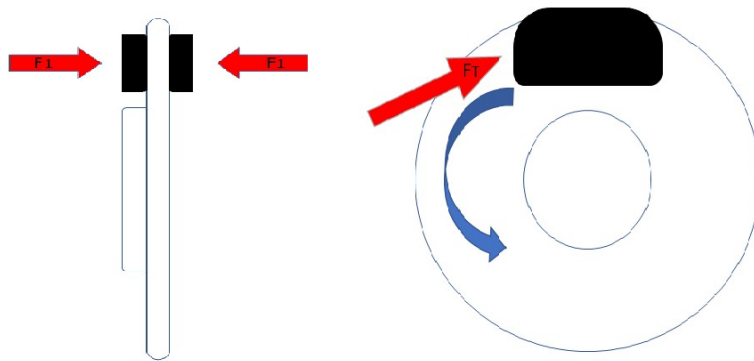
Fuerza de frenado por un caliper sobre el disco.
